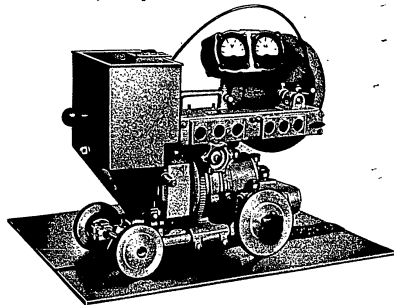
Сварочный трактор TC-17-M, настроенный на сварку стыковых швов без копра
